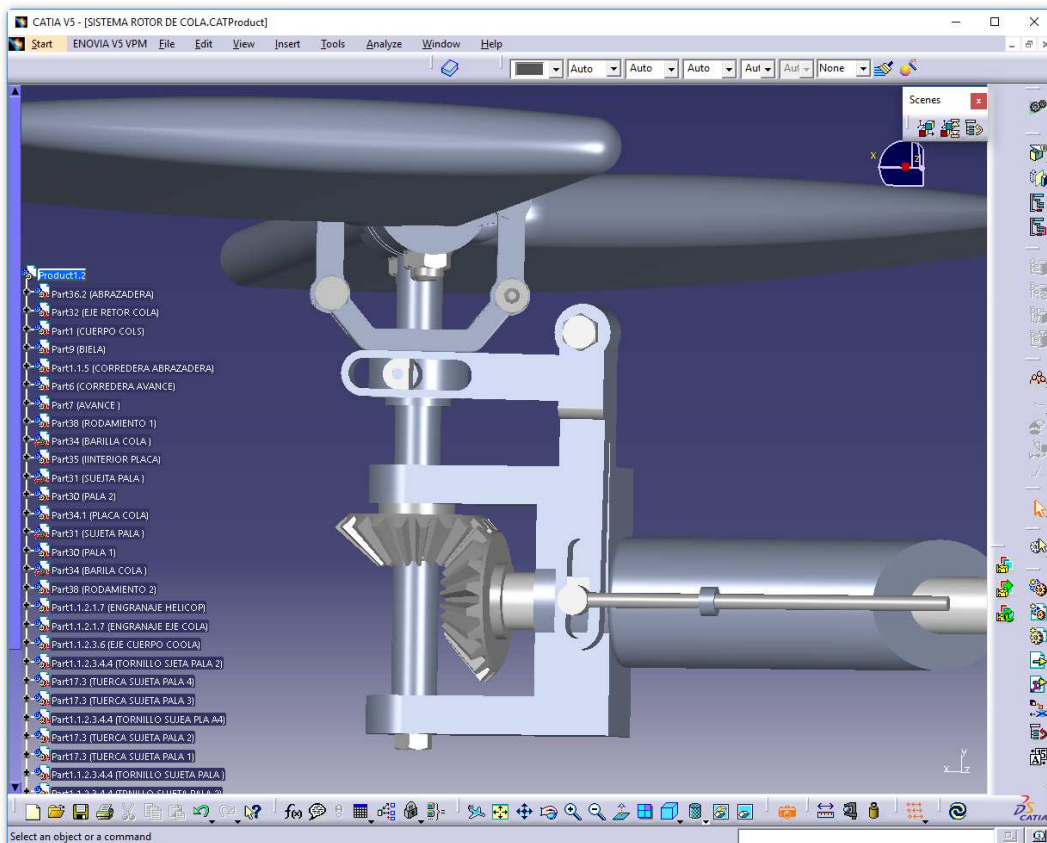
Conjunto sistema rotor de cola – material 2
